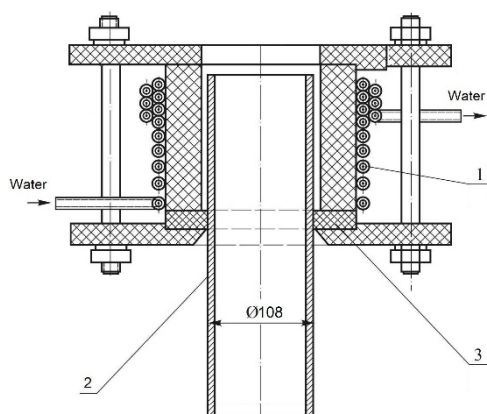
Индуктор для предварительного дифференцированного нагрева трубчатой заготовки: 1 - индуктор, 2 - заготовка, 3 - центрирующее кольцо
